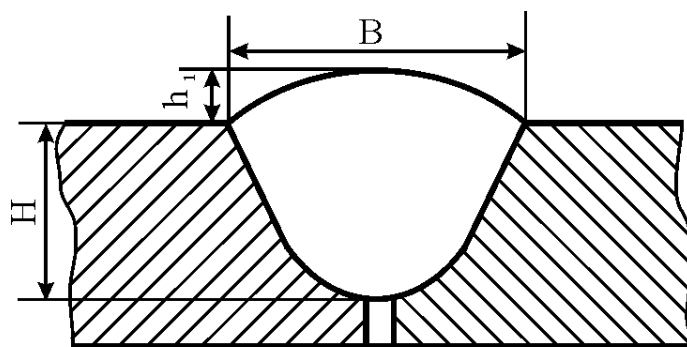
Форма и размеры шва: B – ширина; H – глубина проплавления; h_1 – высота усиления шва
